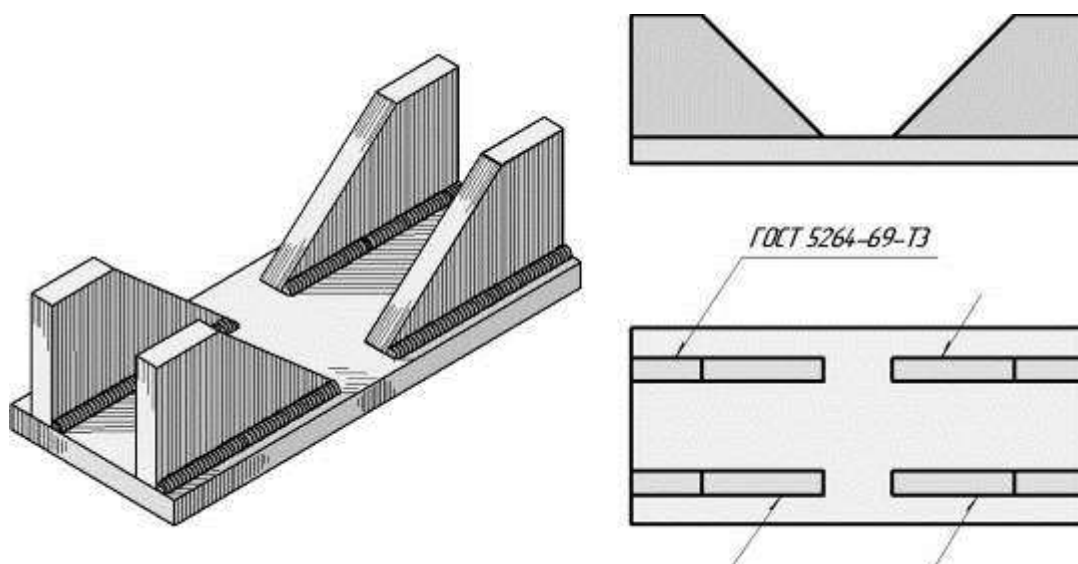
Условное обозначение нескольких одинаковых сварных швов линиями-выносками без полок
